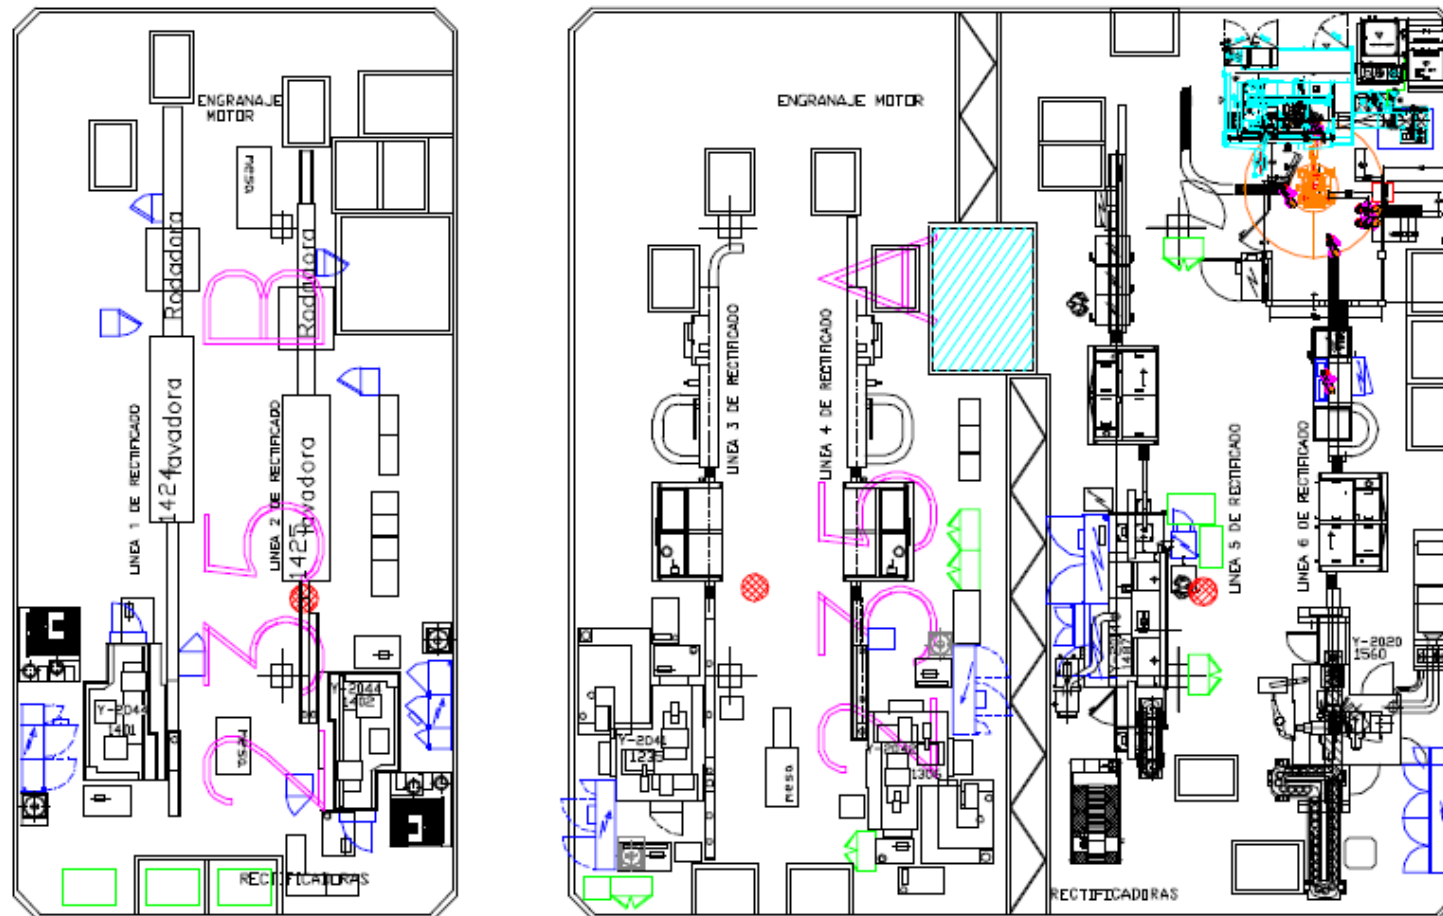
Células 235 B y 235 A de rectificado de engranajes de motor.
